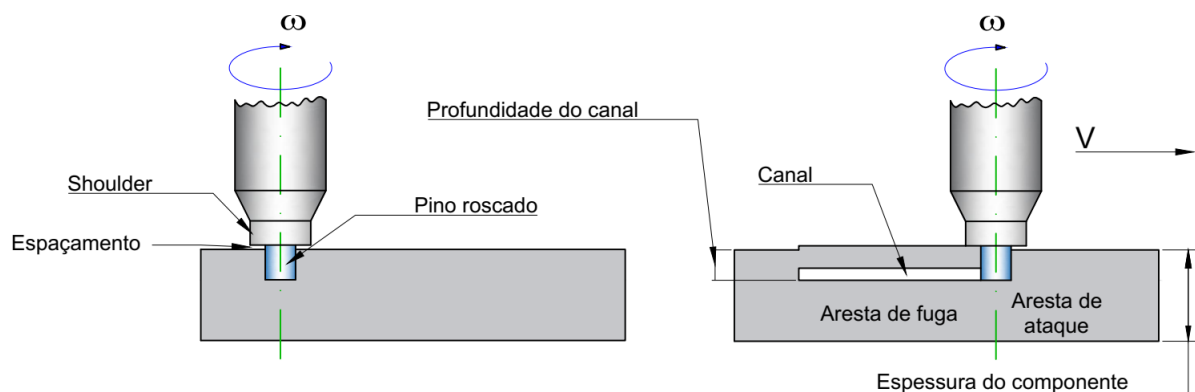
Esquema do *Friction Stir Channeling* with *shoulder* workpiece clearance, adaptado de [18].
